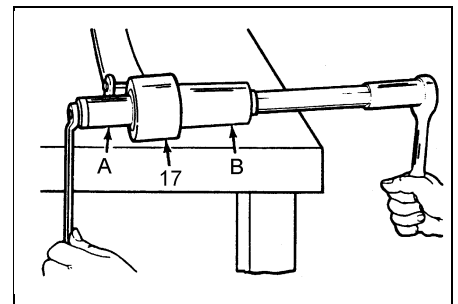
Снятие втулки рессоры. 17 - рессора, А - приспособление для установки и снятия втулок, В - дополнительный упор приспособления.
